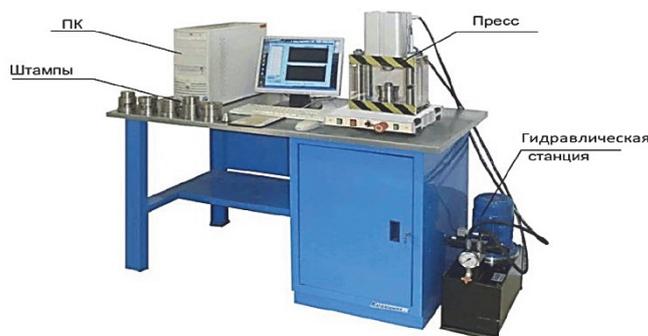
Установка изготовления деталей гидрогазовых систем путем обработки материалов давлением
